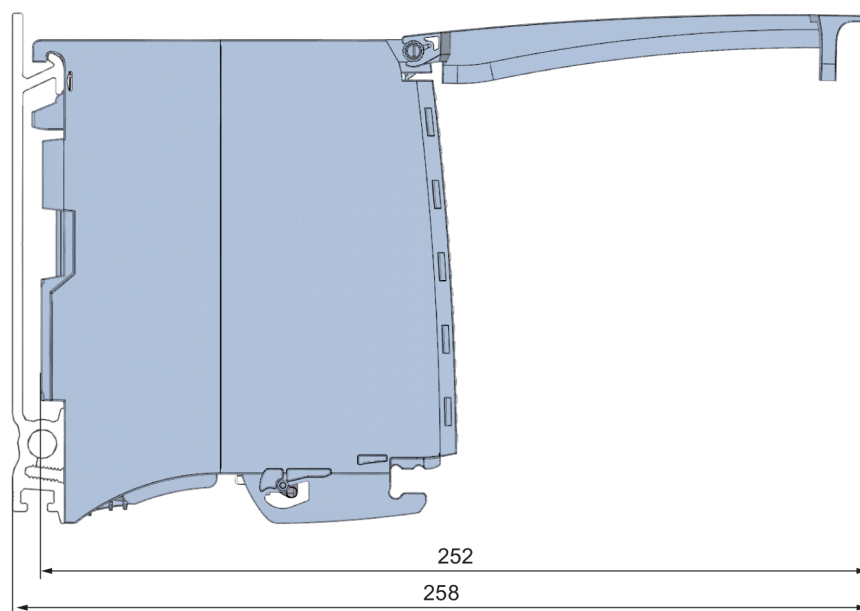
Maßbild des Moduls DI 16x24VDC HF in Seitenansicht mit geöffneter Frontklappe
